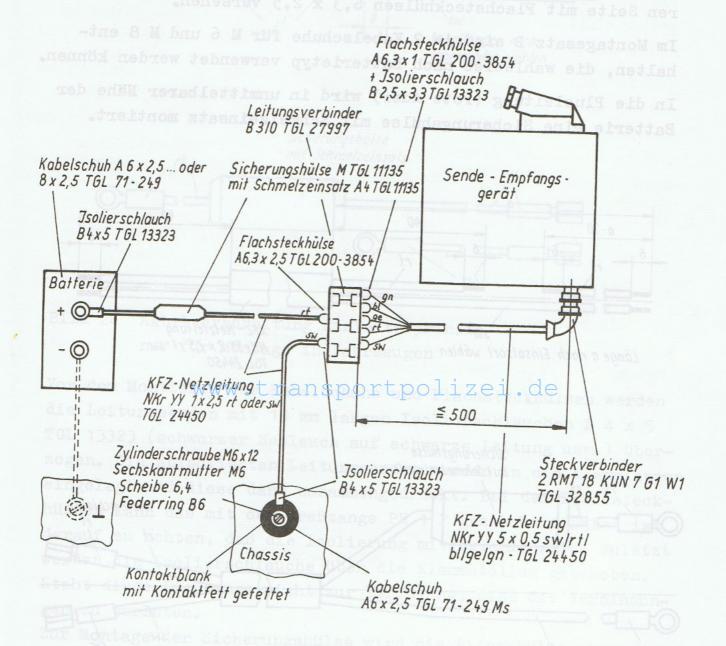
Einleiterprinzip nur für die Montage in Fahrzeugen
